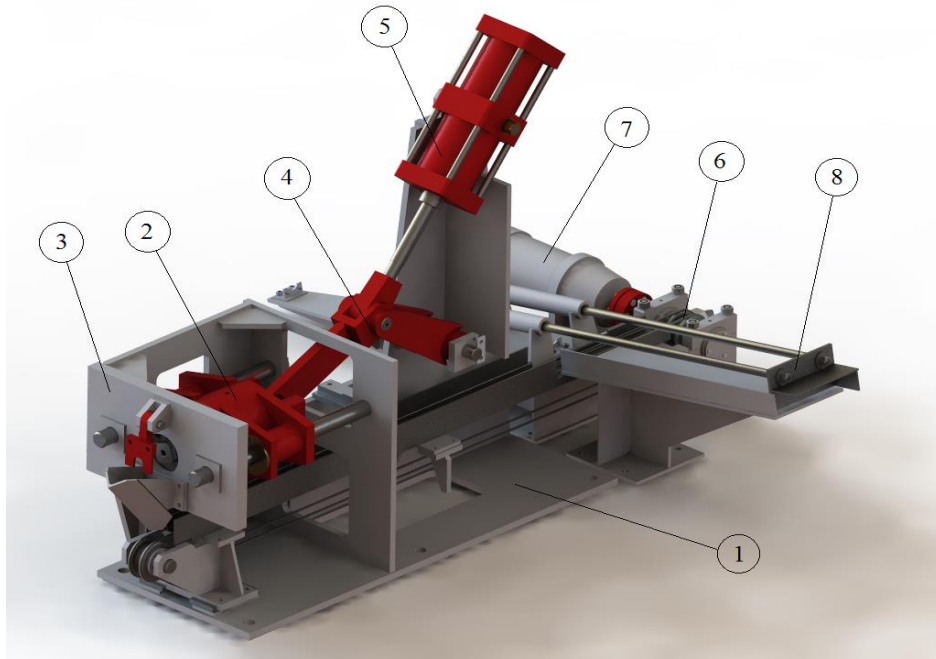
Устройство для получения полых заготовок с дном:
